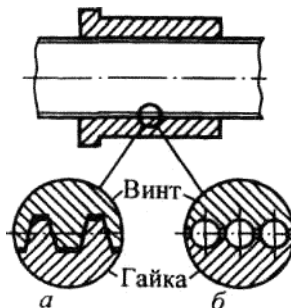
Передача винт-гайка: а — скольжения; б — качения
